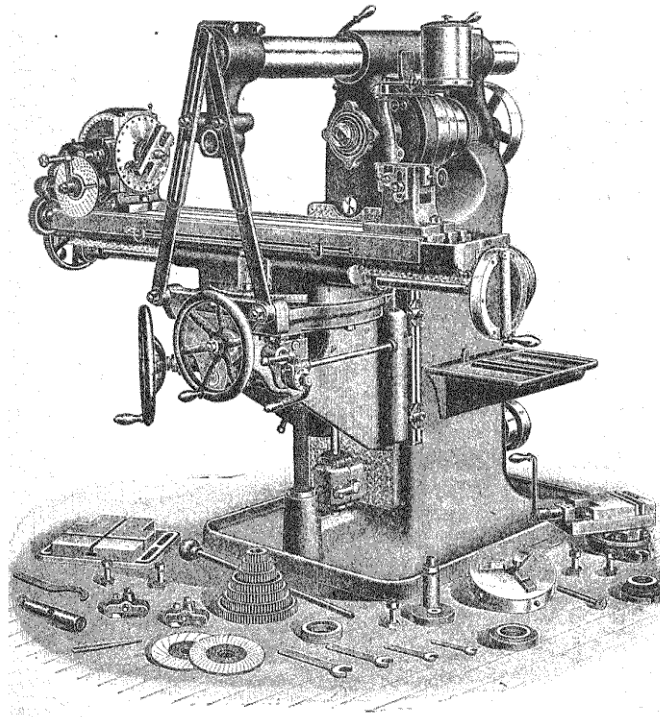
Machine à fraiser universelle Brown et Sharpe.
